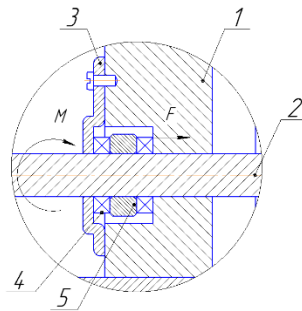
Схема передачі дії гвинт-гайка:
